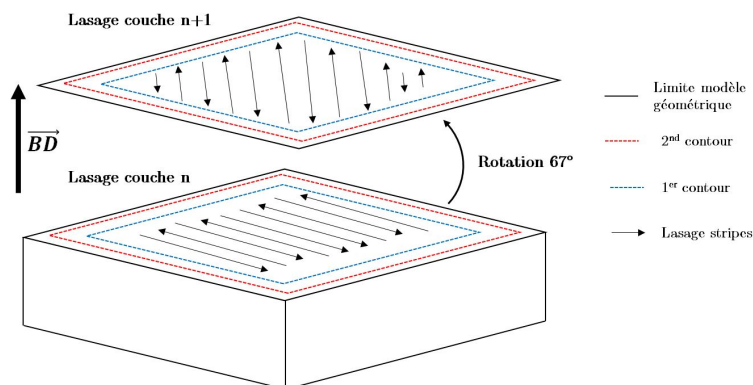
Stratégie de lasage utilisée pour la fabrication des éprouvettes SLM
